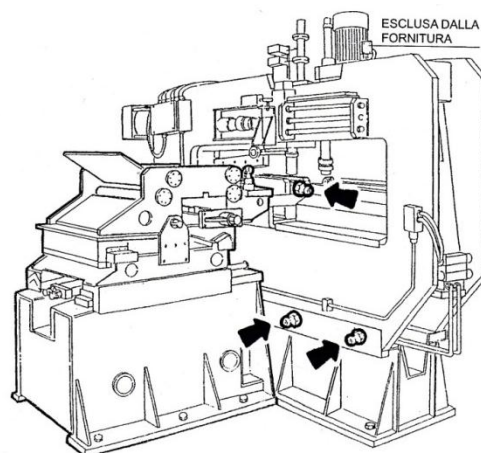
Punto de lubricación de tampón de soldadura
